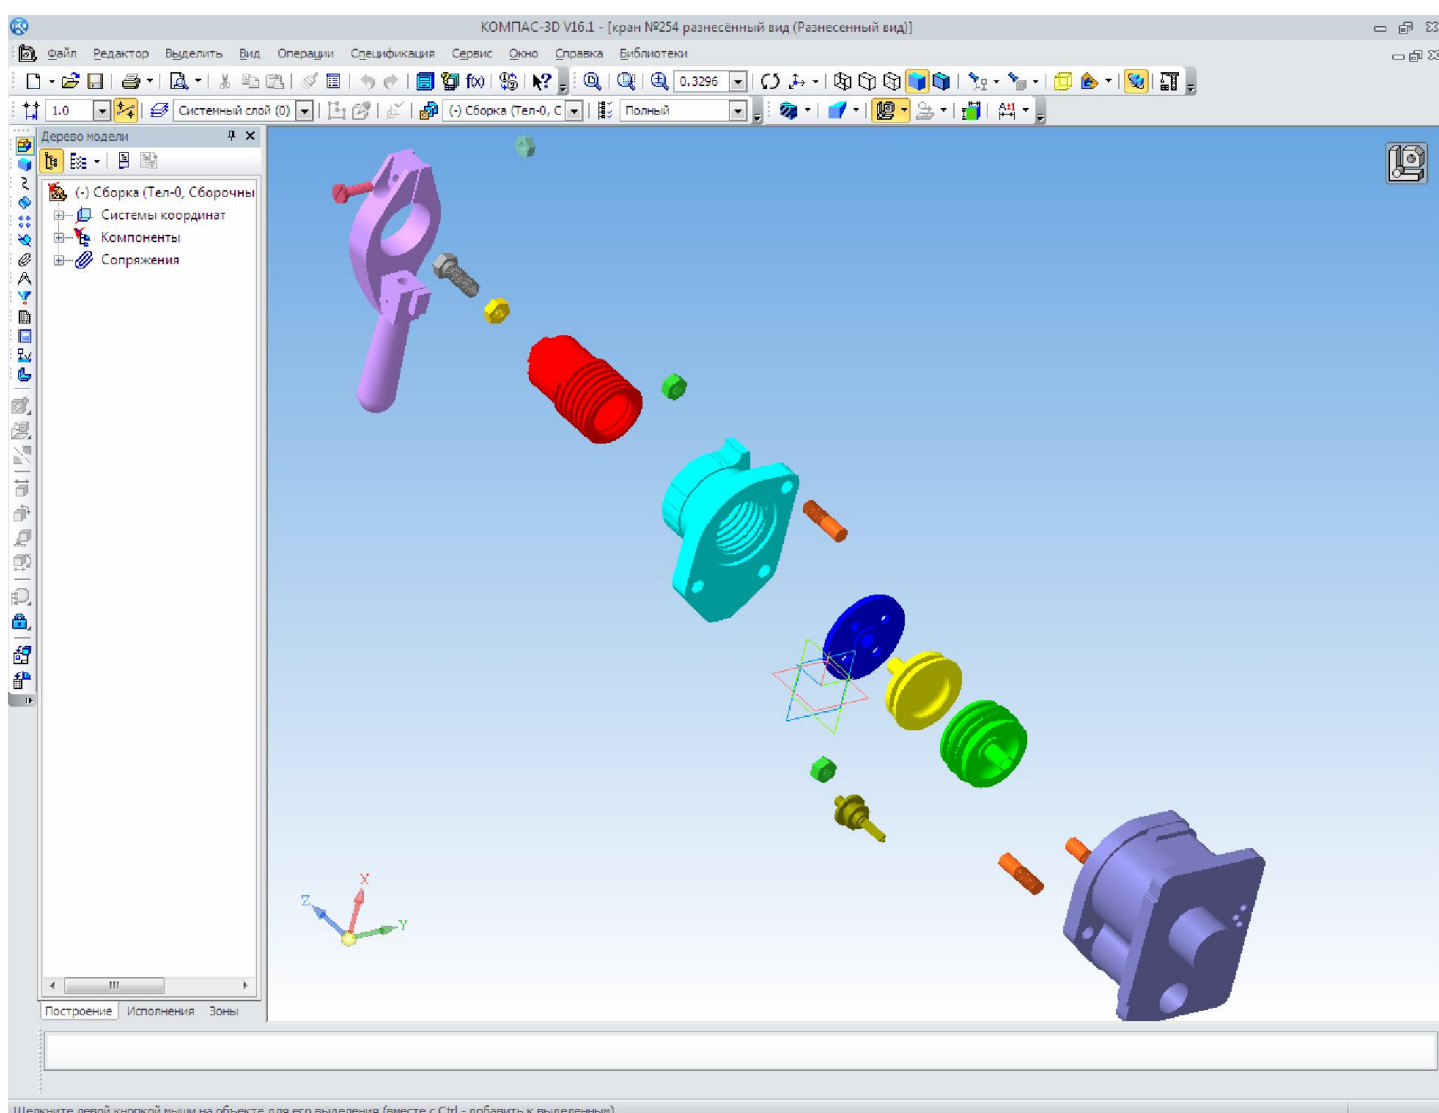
Кран №254 , 3D сборка - разнесенный вид.
